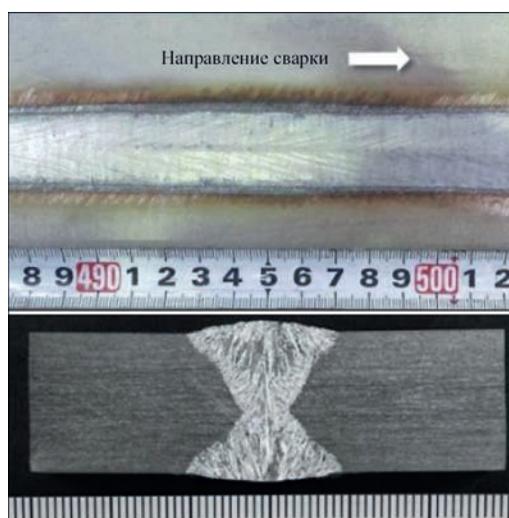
Внешний вид валика сварного шва и макроструктура стыкового соединения US-2209 / PF-S1D (1G)
